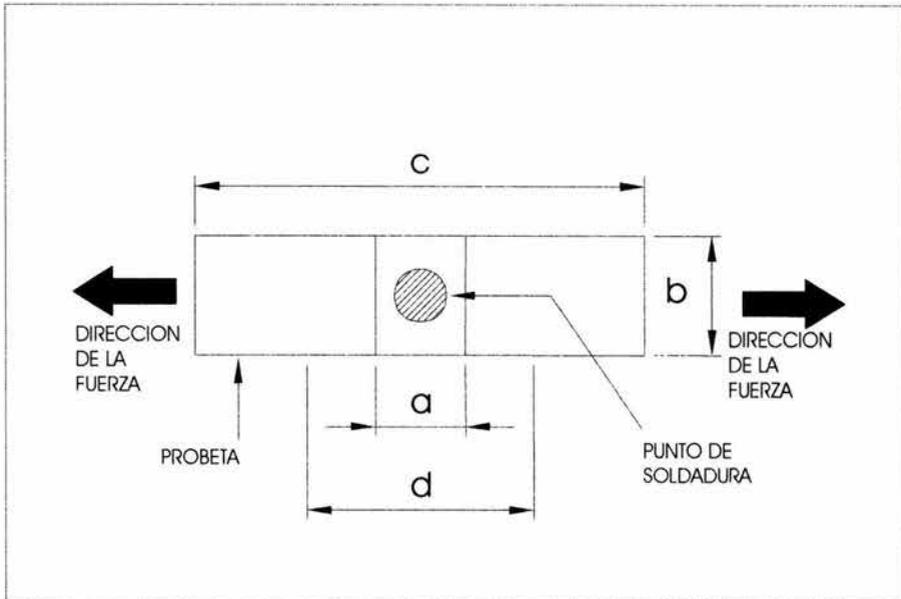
Esfuerzo cortante aplicado a un punto de soldadura.
